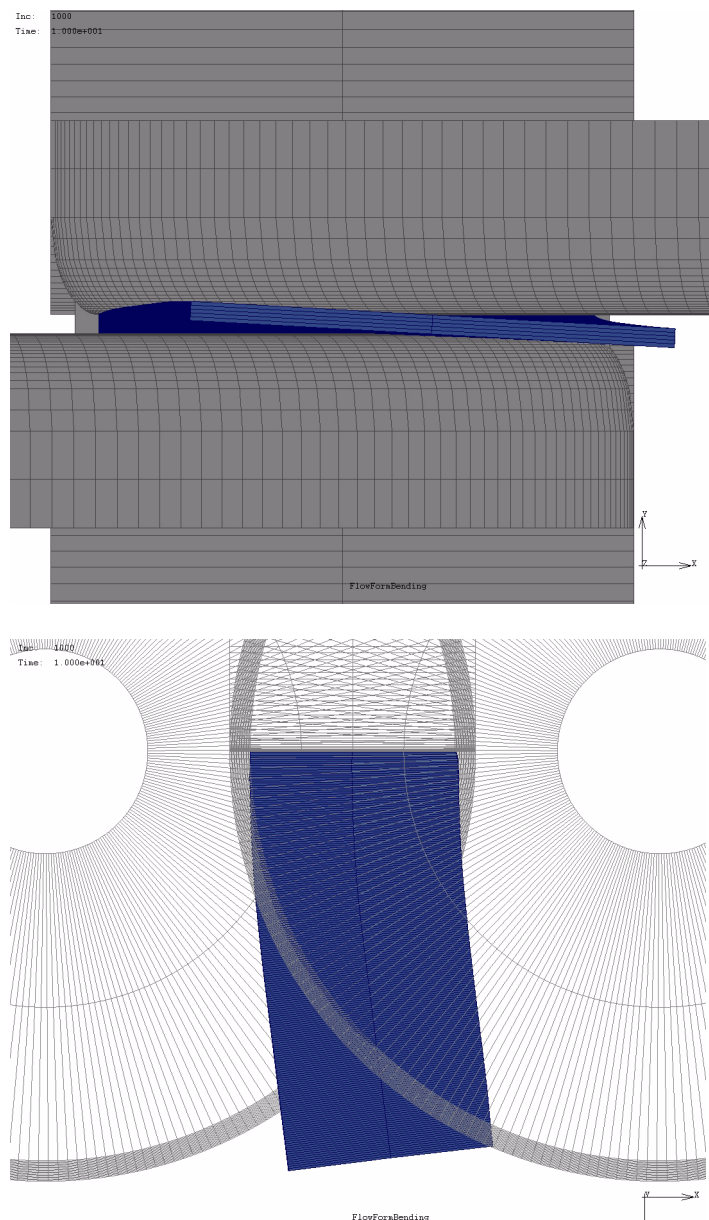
Querrolle/Querrolle - Frontansicht (oben) und Draufsicht (unten)
